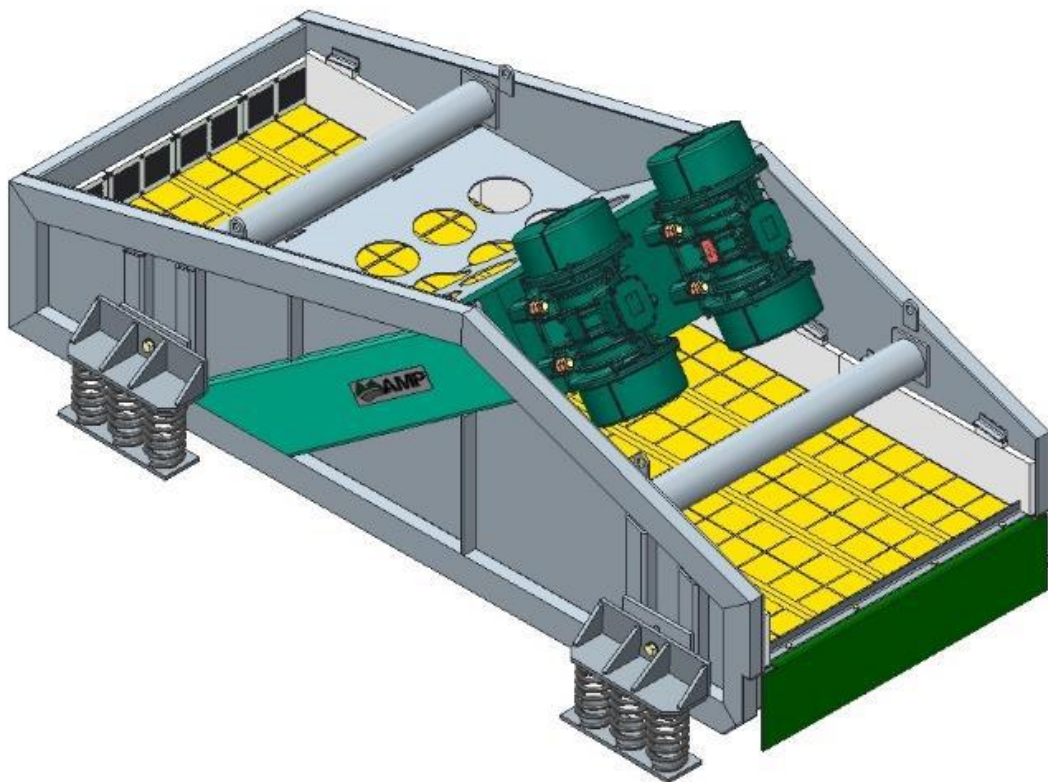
Ecurridor planta piloto (fuente : AMP)
